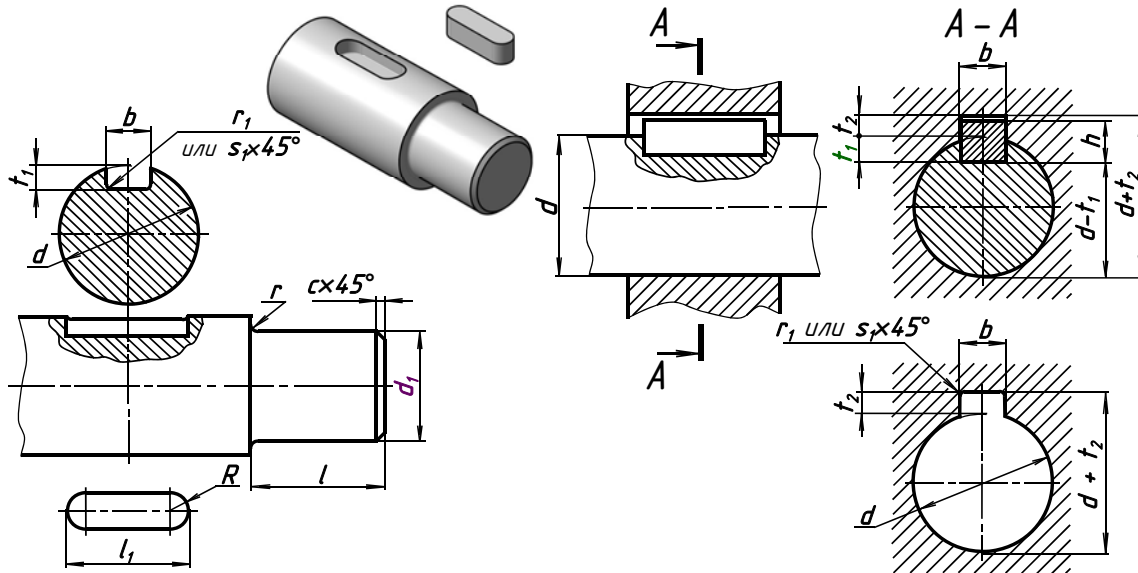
Выполнение согласно чертежу конструктивных элементов вала токарной и фрезерной обработкой и сверлением заготовки, полученной на 3-й стадии изготовления
